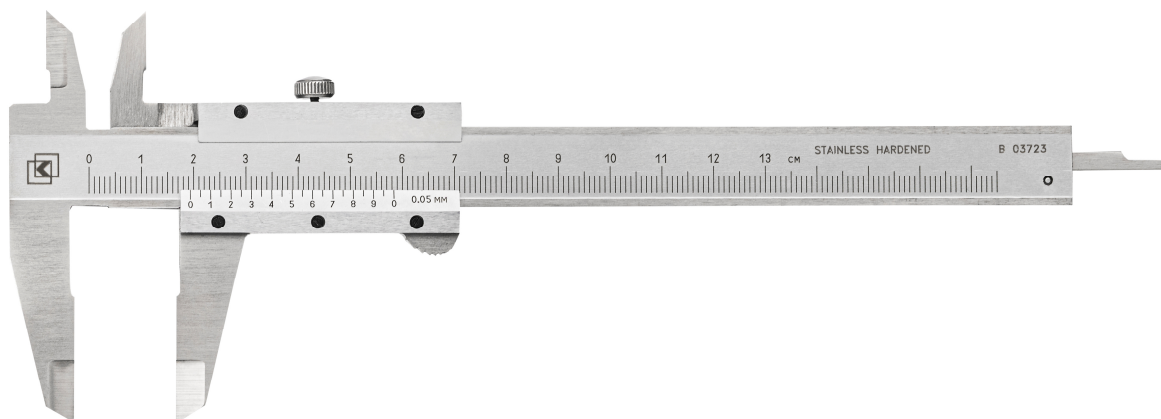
Общий вид штангенциркулей ШЦ-I
